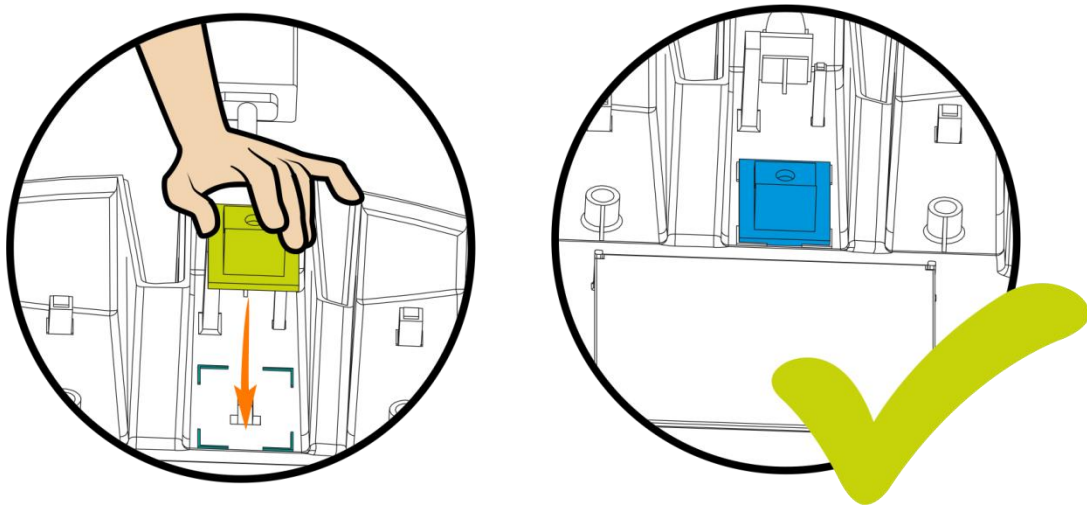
Ensamblaje 1.11 – 1.4
